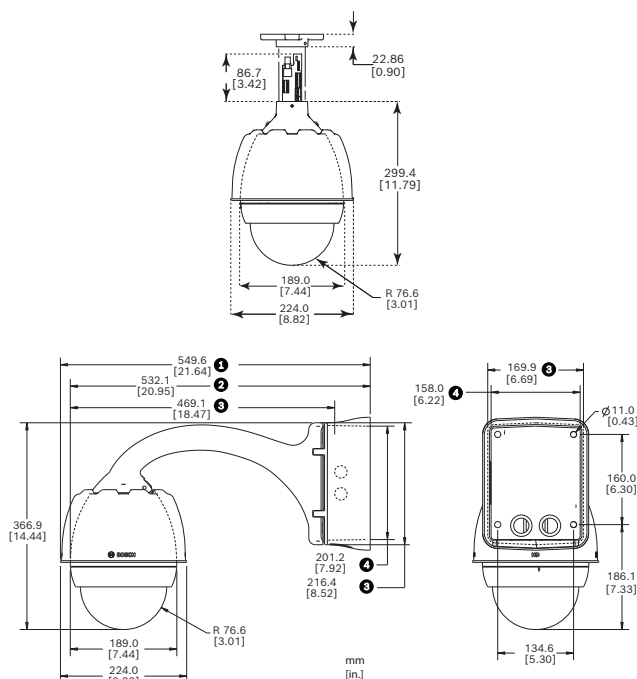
Dimensioni, AUTODOME7000, montaggio su tubo, montaggio pendente
